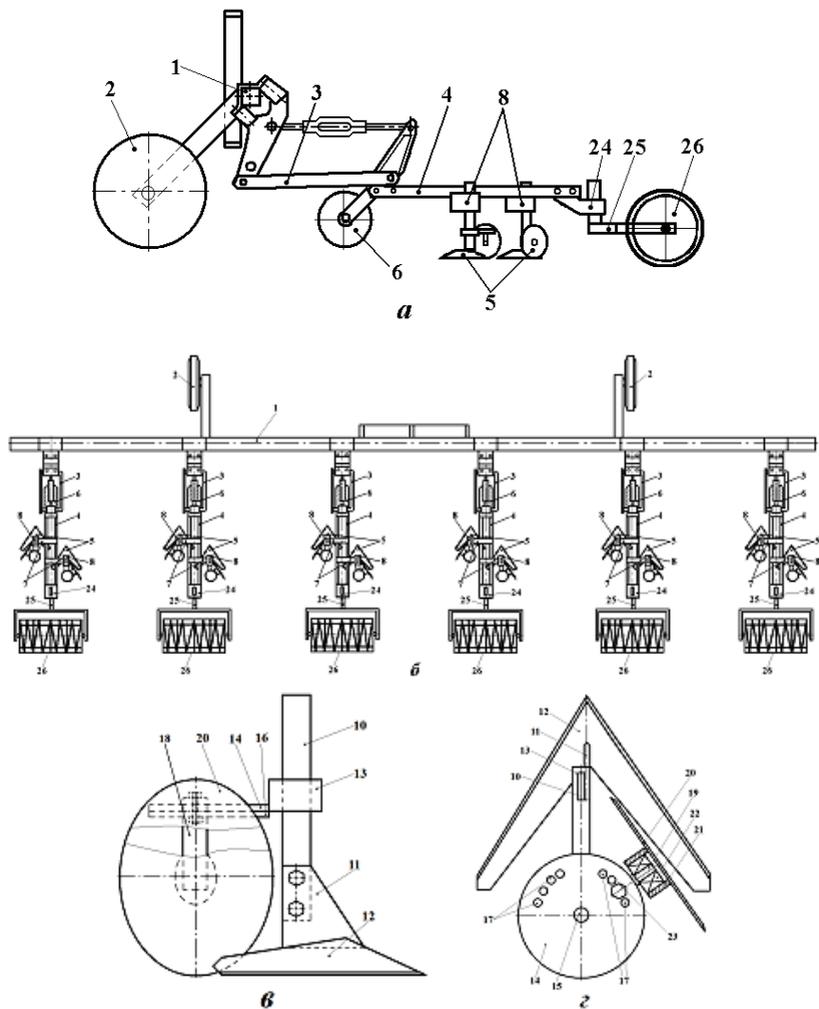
Пропашной культиватор (обозначения в тексте): а – вид сбоку; б – вид сверху; в – рабочий орган культиватора, вид сбоку; г – рабочий орган культиватора, вид сверху
